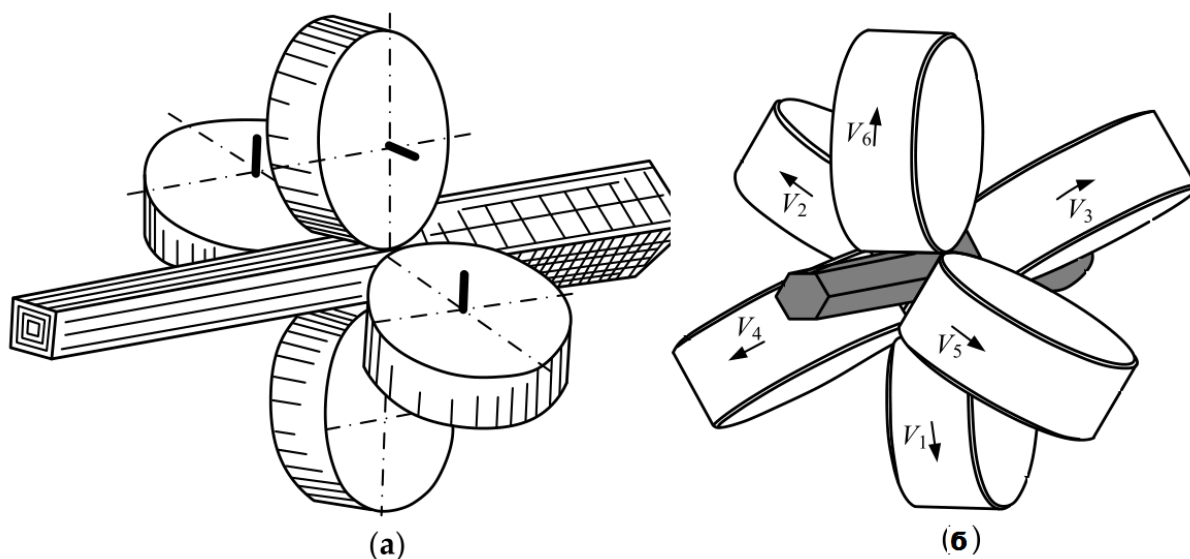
Схема прокатки заготовки а) квадратної форми: у чотирьохвалковому калібрі; б) шестигранної форми – у кліті з шестивалковим калібром.
